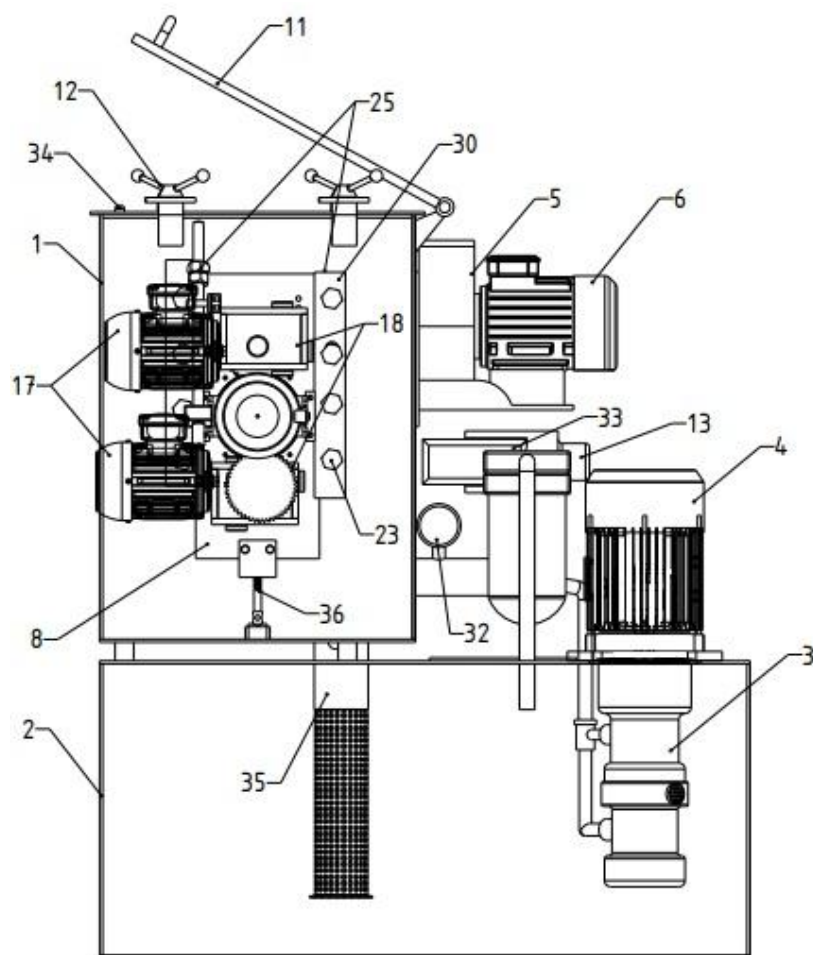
Установка для ГДУ (вид спереди)
